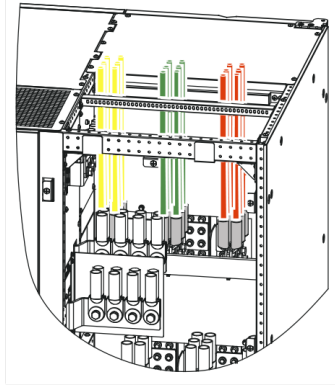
Cableado de entrada de bypass del UPS-IND HF 13800
